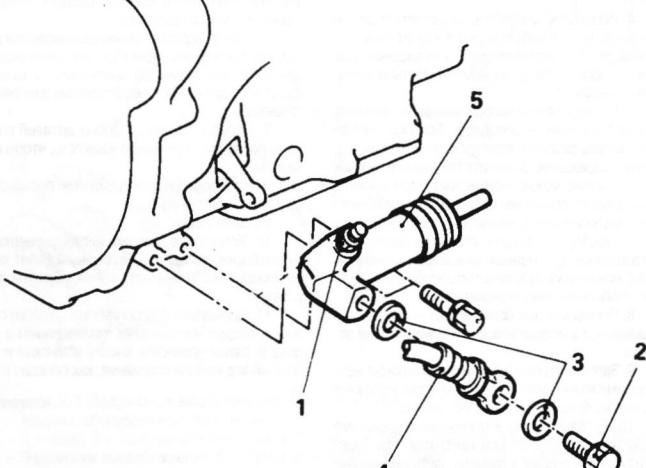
Подробности установки цилиндра высвобождения сцепления
